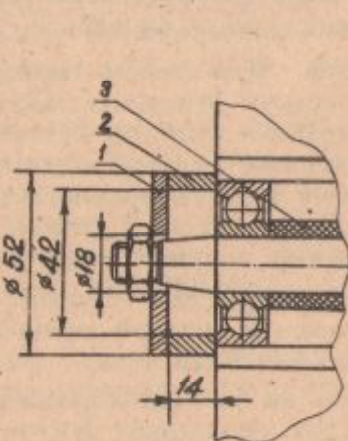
Допрессовка коленчатого вала в левую половину картера:
